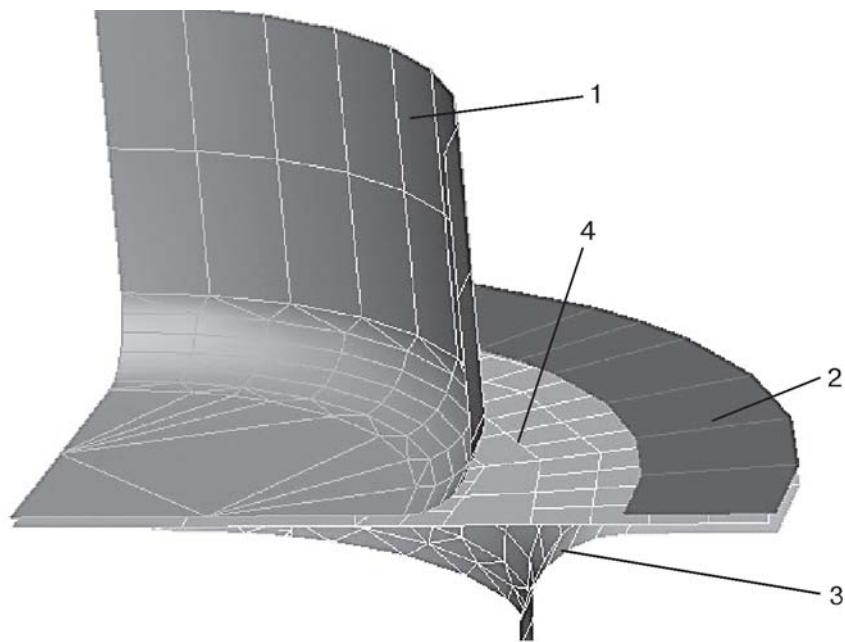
Конечно-элементные модели инструмента и заготовки в программном комплексе PAM-STAMP:
